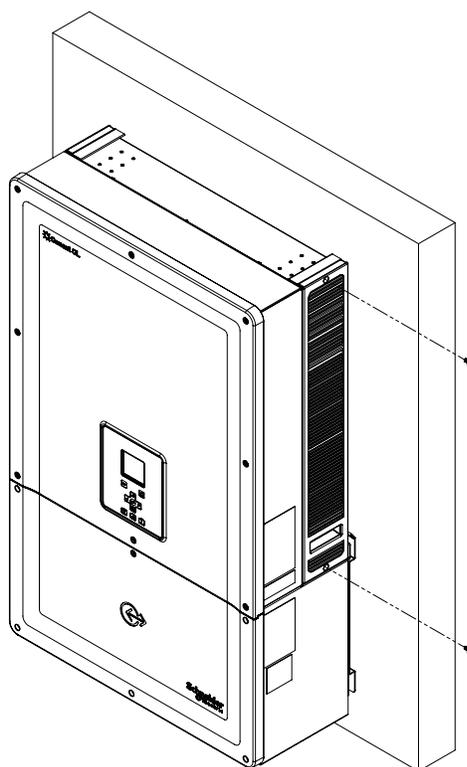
Desserrage des vis du couvercle de la grille d'aération – côté droit
